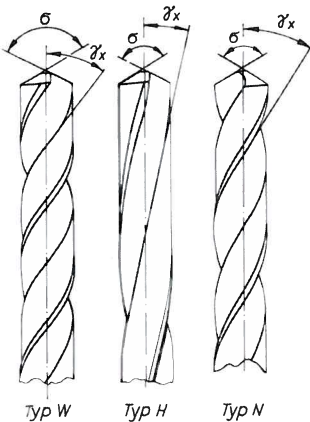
Wendelbohrerausführungen. Für die Aluminiumbearbeitung ist der Typ W geeignet
